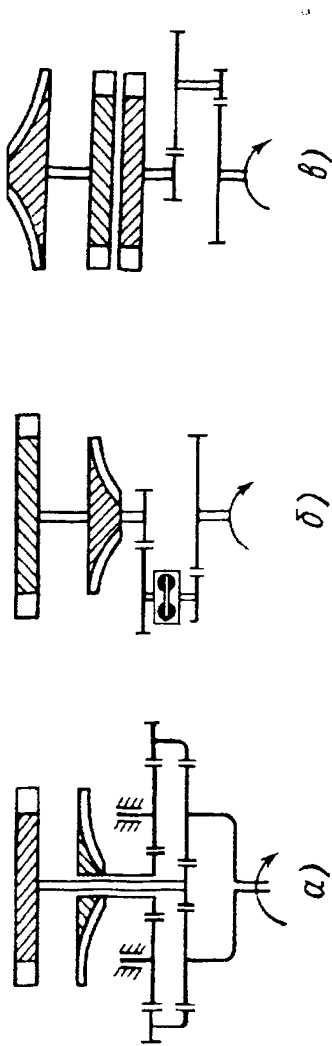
Кинематические схемы турбокомпрессорных стартеров:
